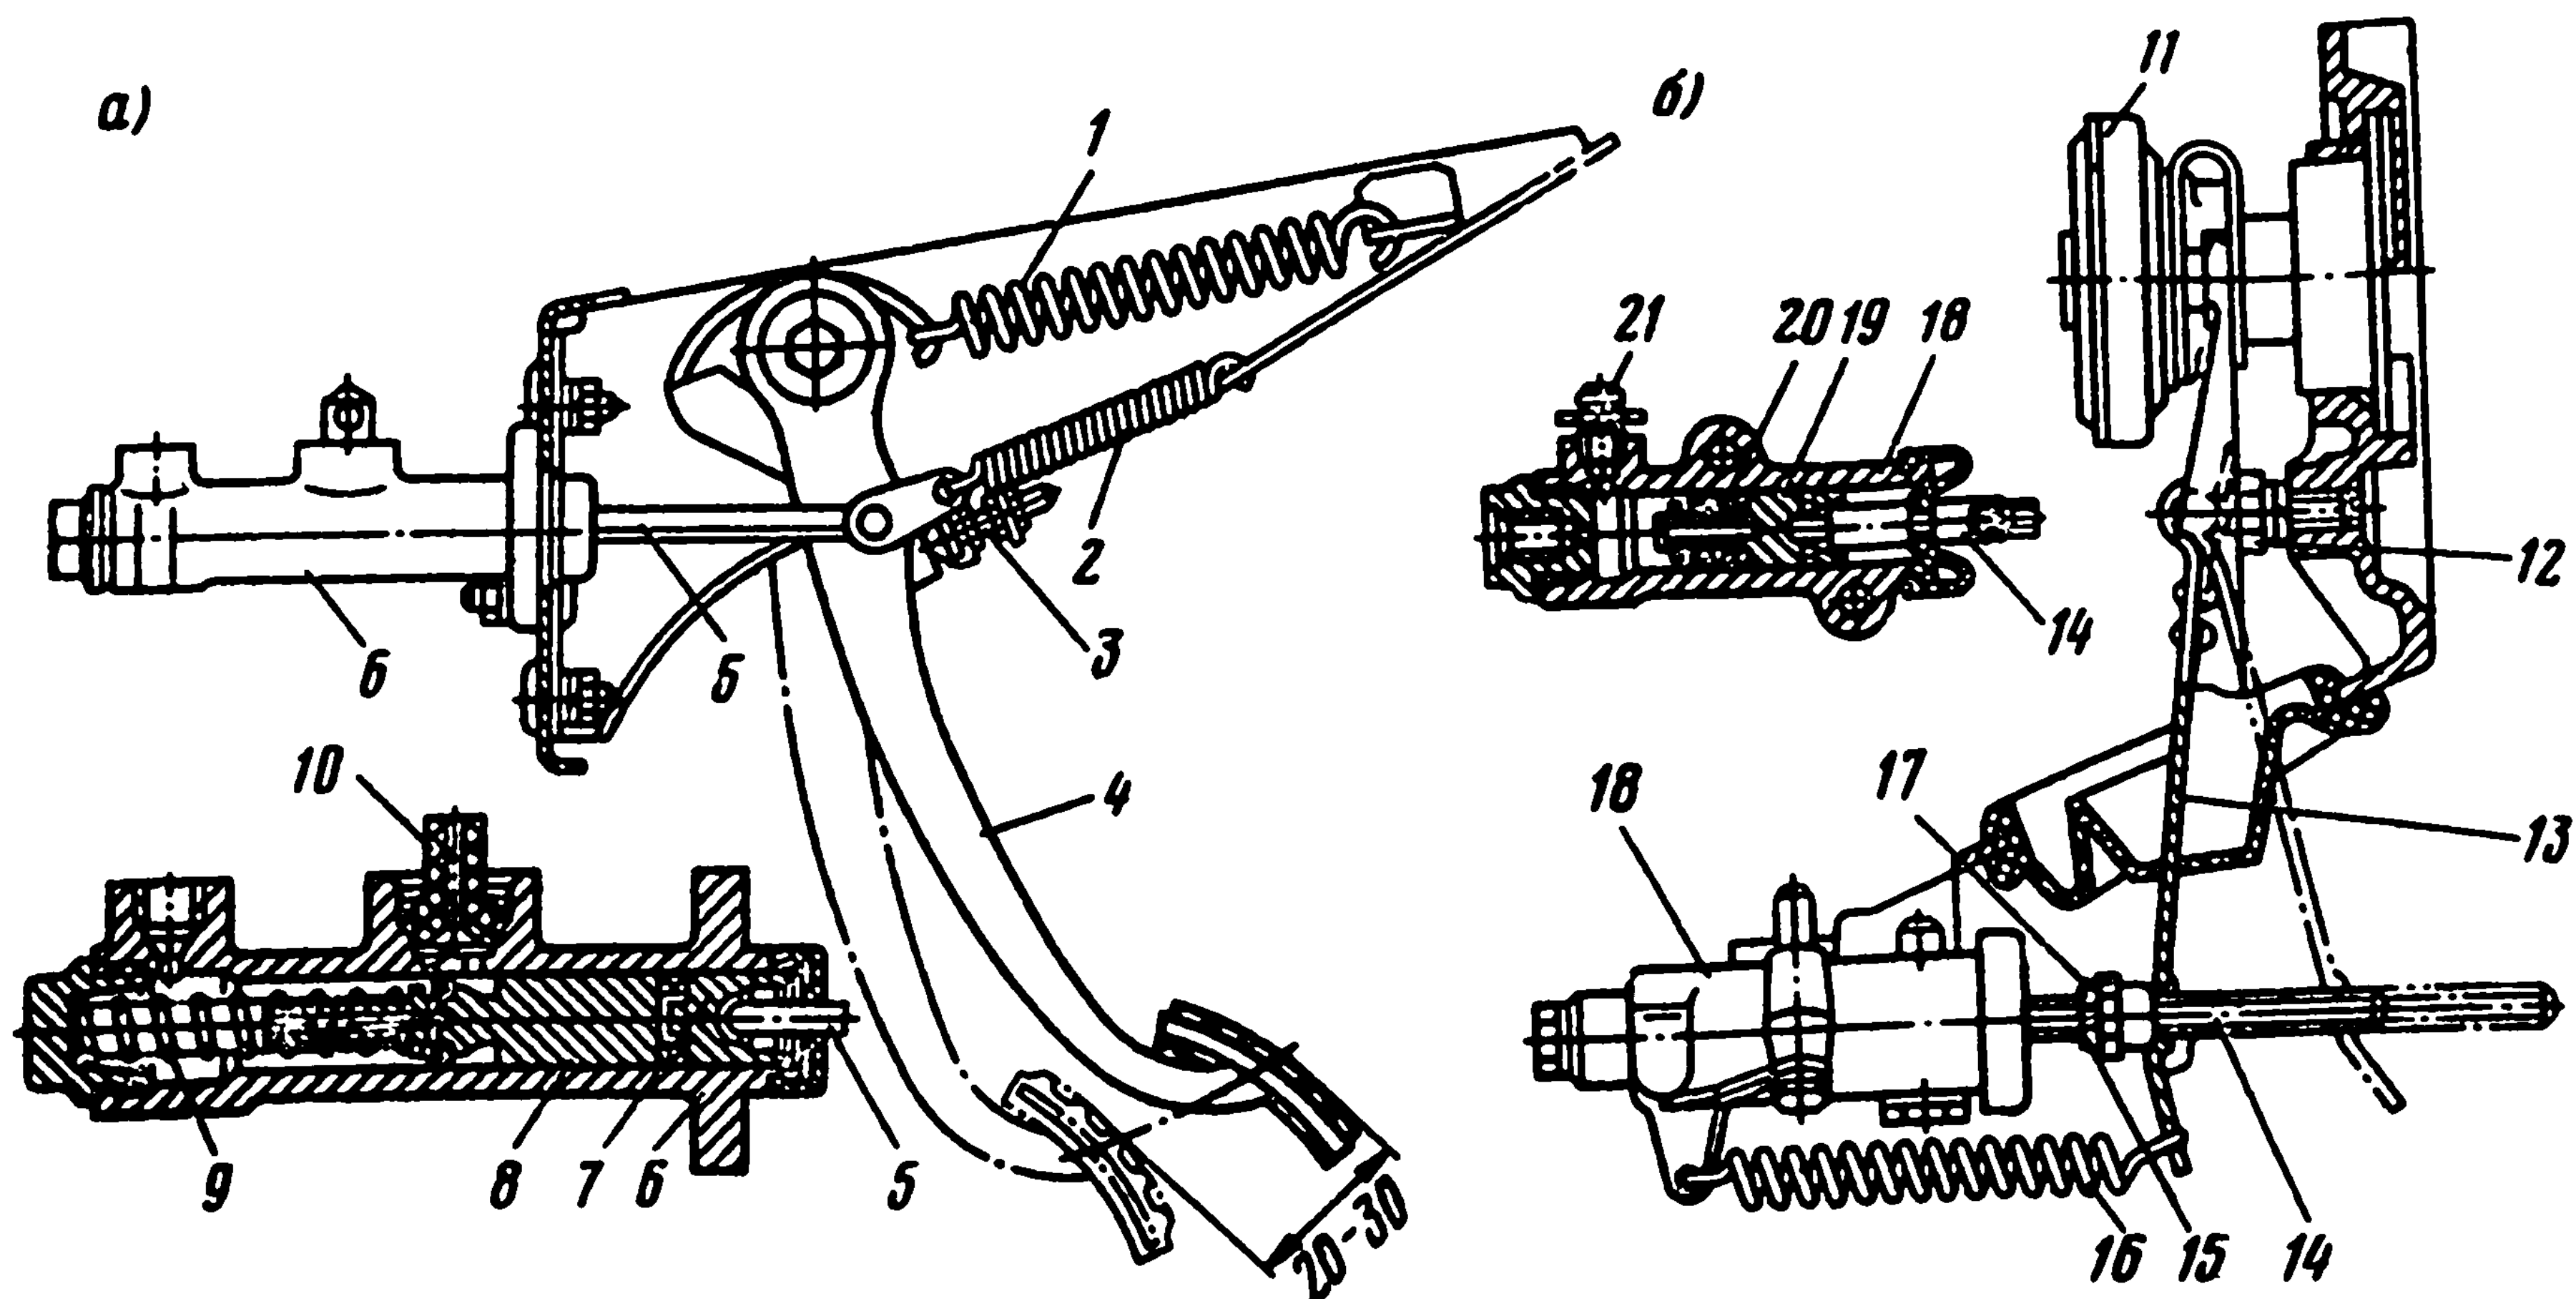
Привод сцепления автомобиля ВАЗ-2121:
